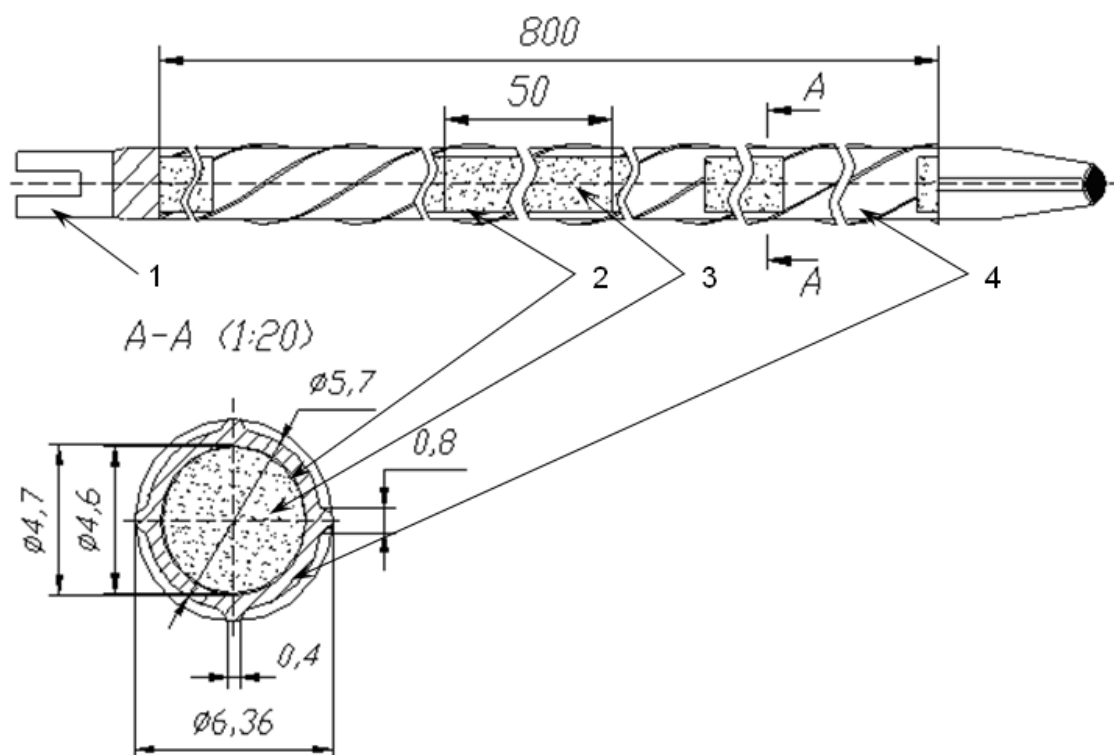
Схема керметного твэла: 1-концевые детали; 2-контактный под-
